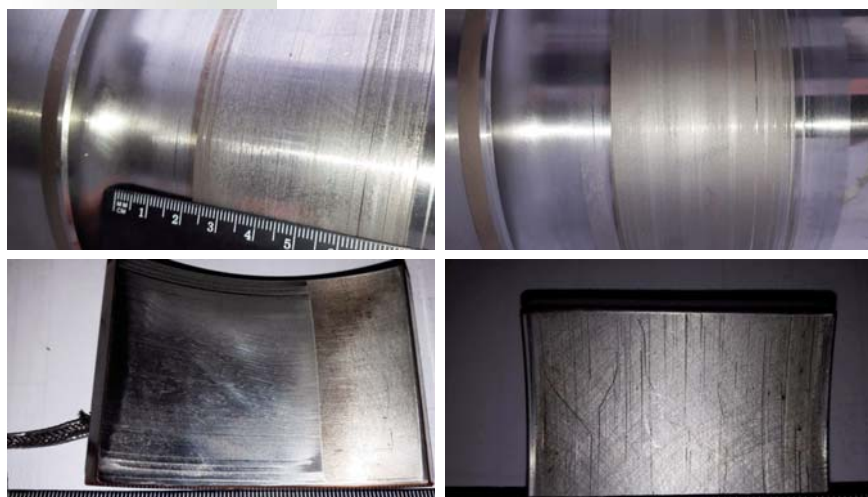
Повреждение сегментов подшипника и шейки ротора осевого турбокомпрессора Elliott
